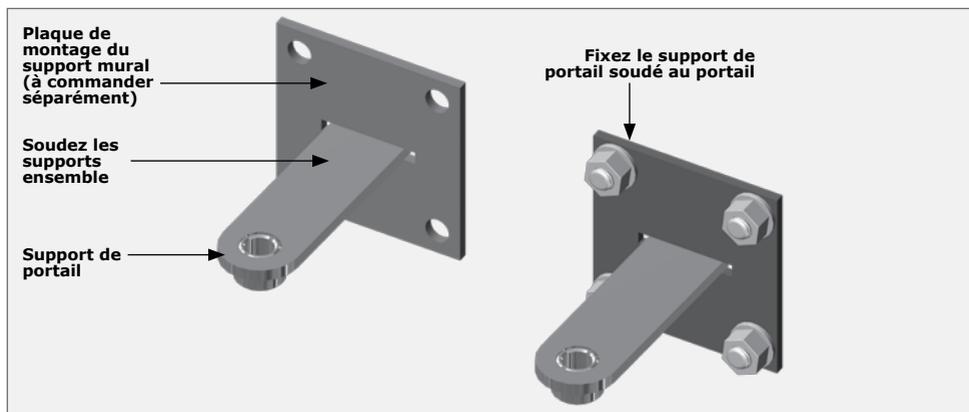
FIXATION DU SUPPORT DE PORTAIL SUR UN PORTAIL QUI N'EST PAS EN ACIER
